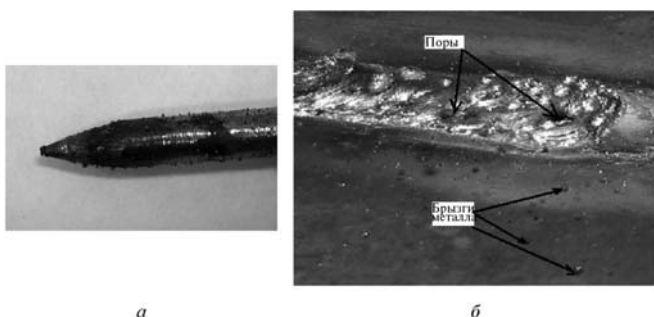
Внешний вид поверхности дефектного вольфрамового электрода (а) и сварного шва, выполненного аргонодуговой сваркой неплавящимся электродом (б) [2]
